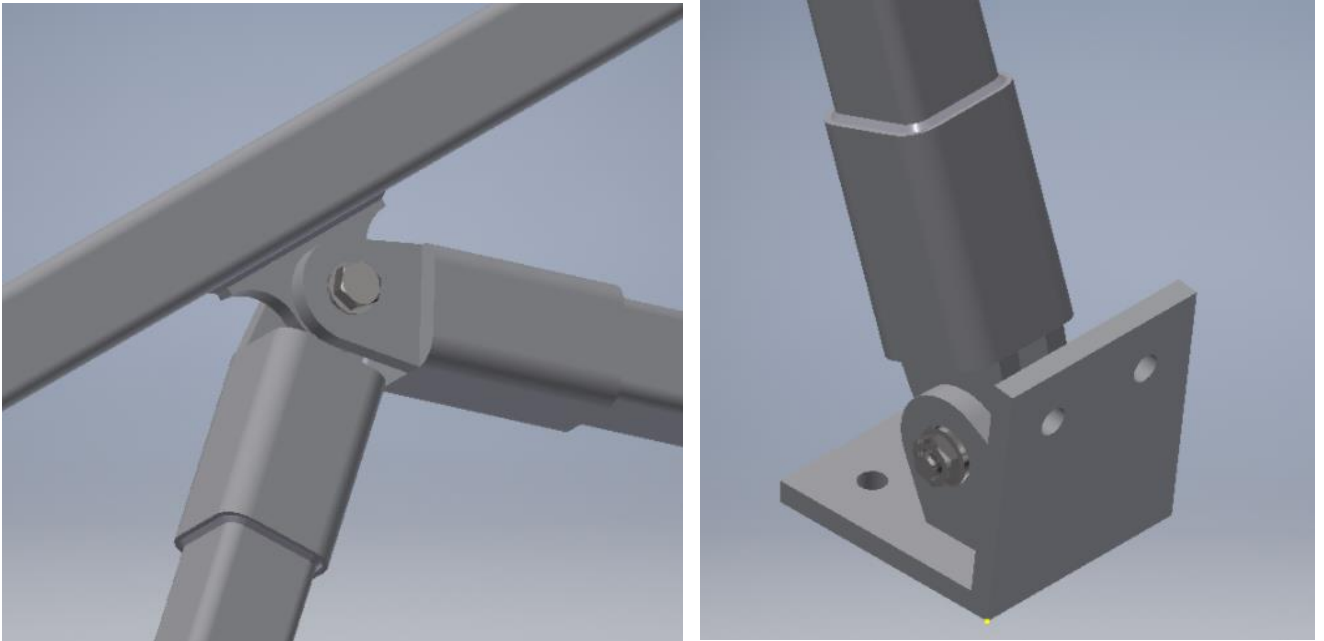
Detalles de unión del larguero (izquierda) y apoyo con la cubierta (derecha).
